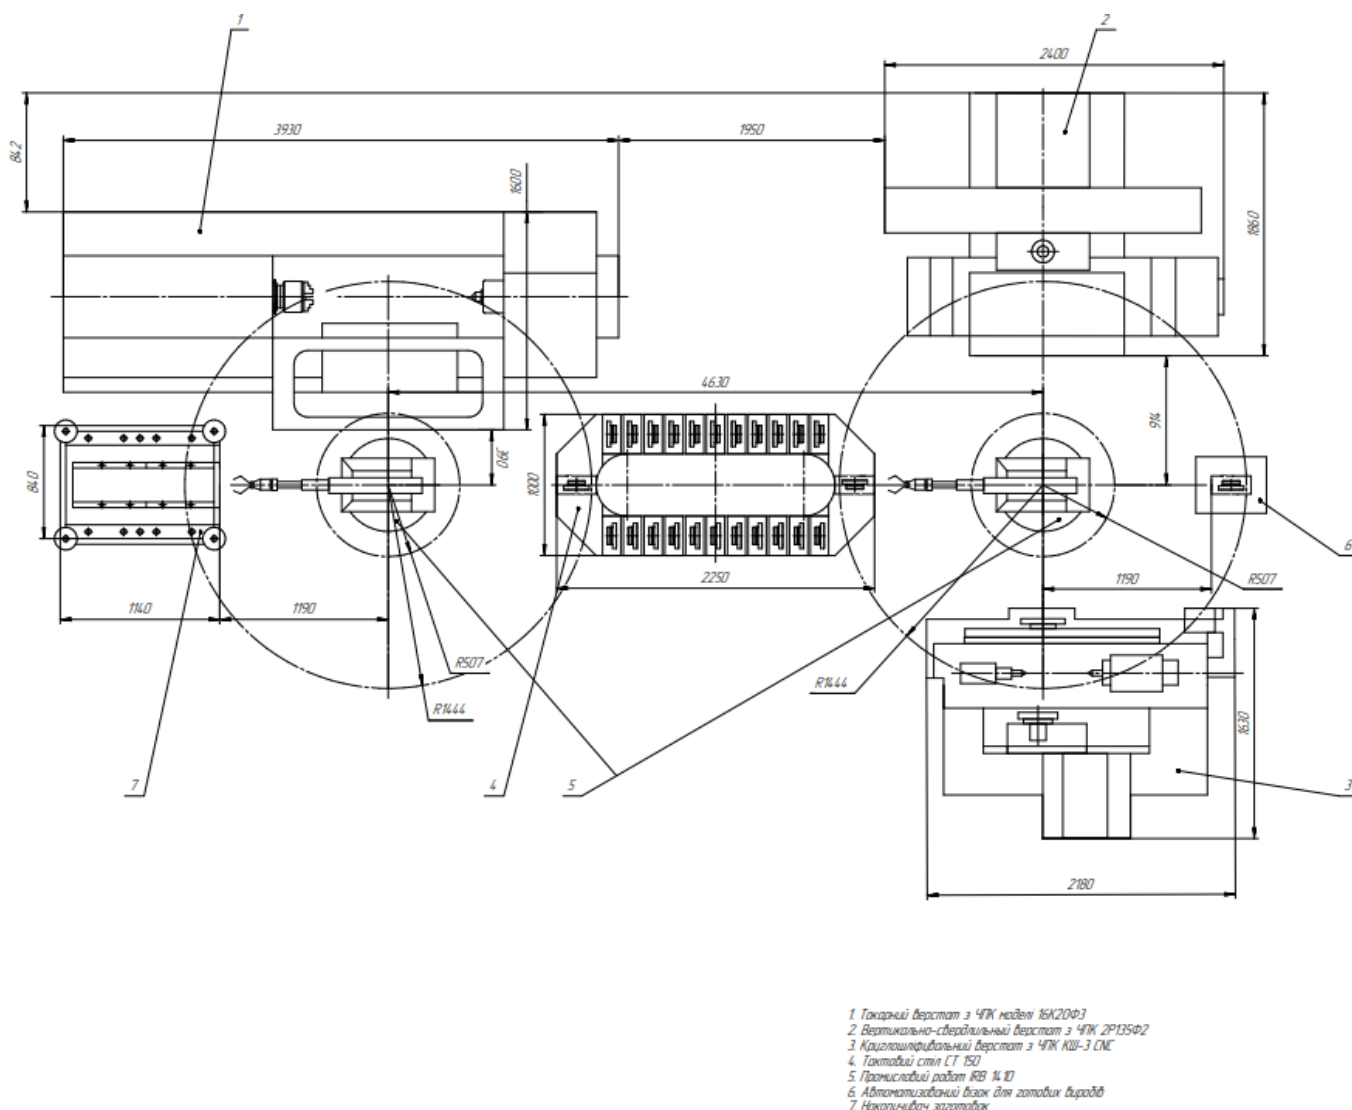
Планування РТК виготовлення деталі «Кришка підшипника»
